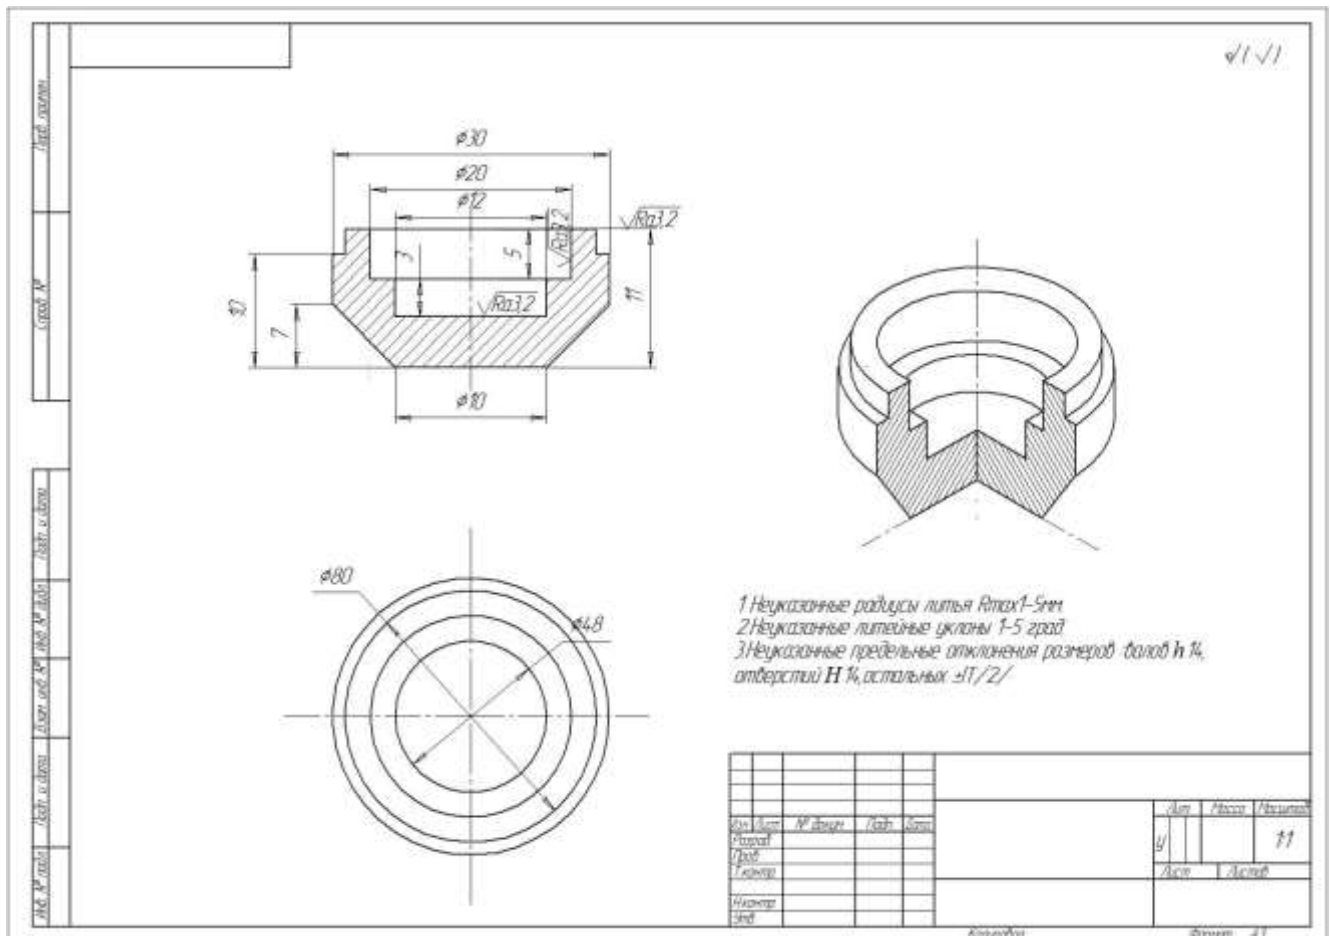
Рабочий чертеж и аксонометрия с вырезом одной четверти .
